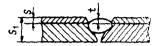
Усиление переходного слоя в сварных соединениях двухслойных сталей
